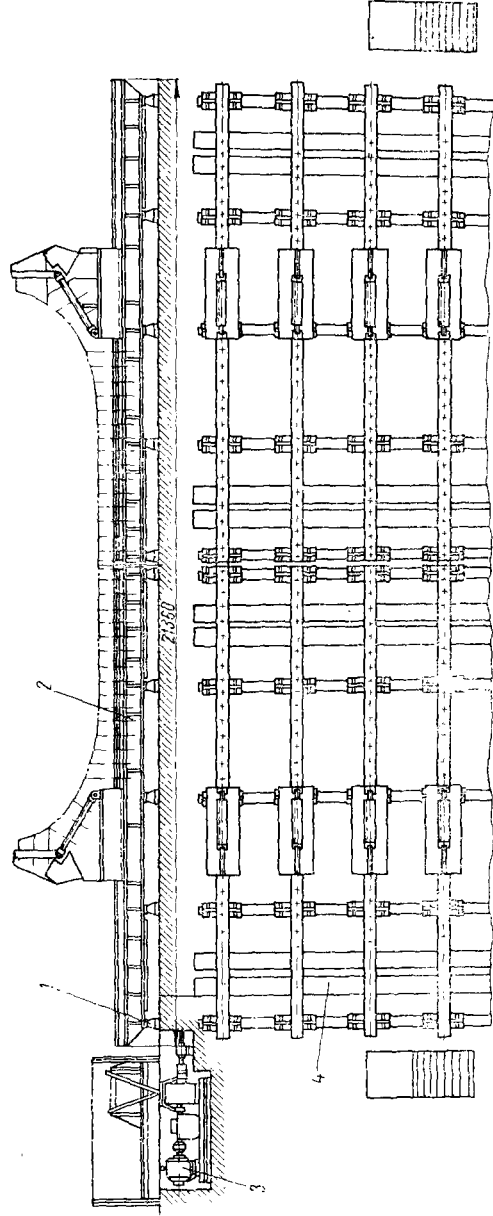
Универсальная постель для сборки и сварки днищевых секций
